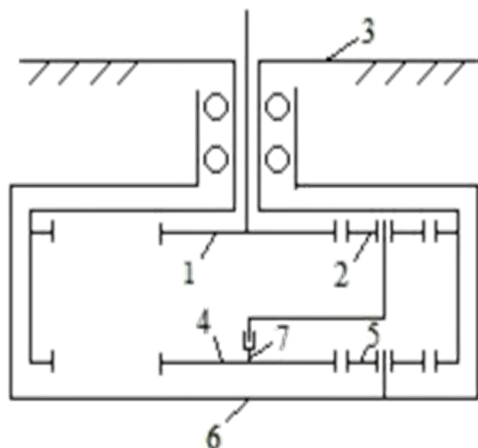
Кинематическая схема двухступенчатого планетарного редуктора: 1 – вал-шестерня 1^{ой} ступени; 2 – сателлит 1^{ой} ступени; 3 – эпициклическое колесо; 4 – шестерня 2^{ой} ступени; 5 – сателлит 2^{ой} ступени; 6 – водило 2^{ой} ступени; 7 – водило 1^{ой} ступени
